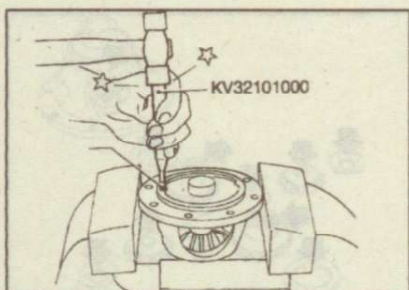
Установка цилиндрического штифта крепления оси сателлитов
